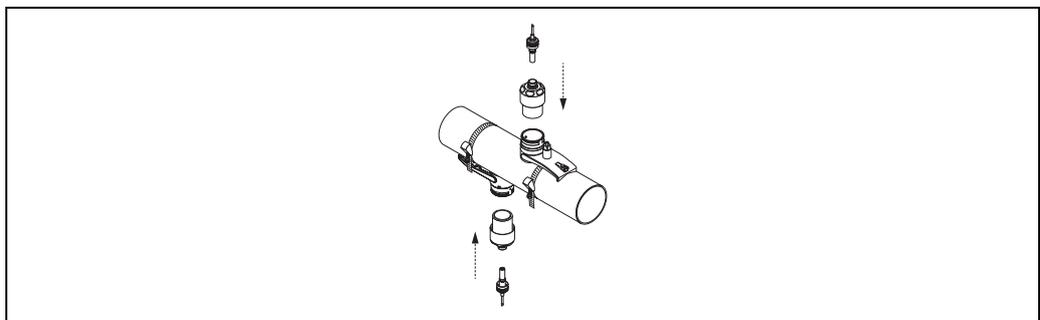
Montaggio del sensore e collegamento del cavo di collegamento
